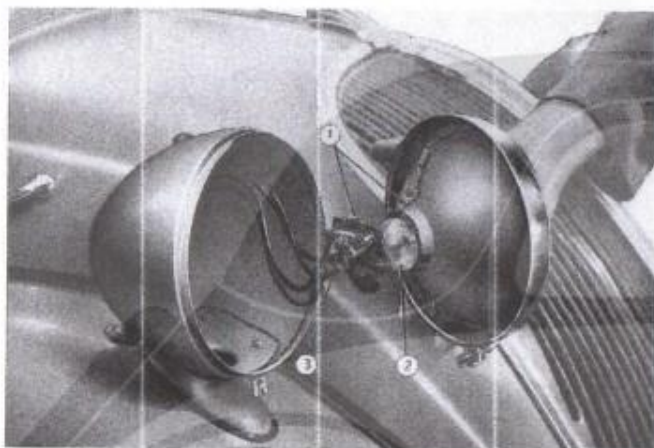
Smontaggio del supporto delle lampadine dai proiettori.
